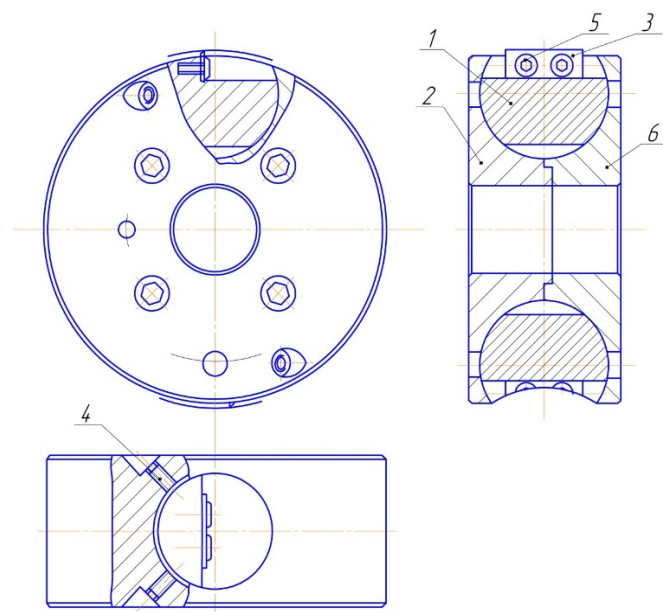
Фреза сборная с адаптивными свойствами (изменяемыми углами):
